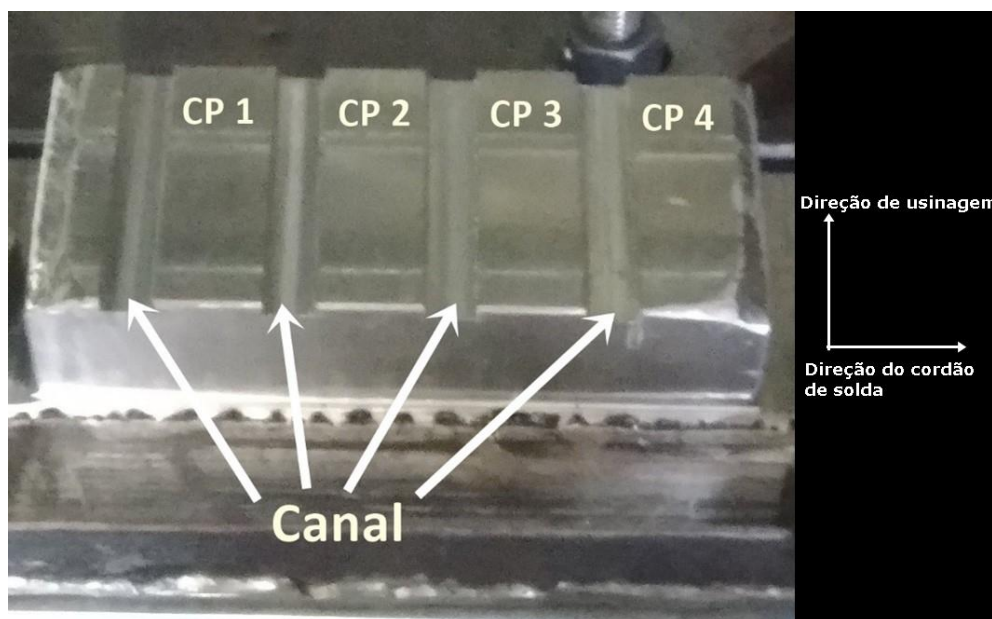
Bloco de Inconel 625 produzido por soldagem.
